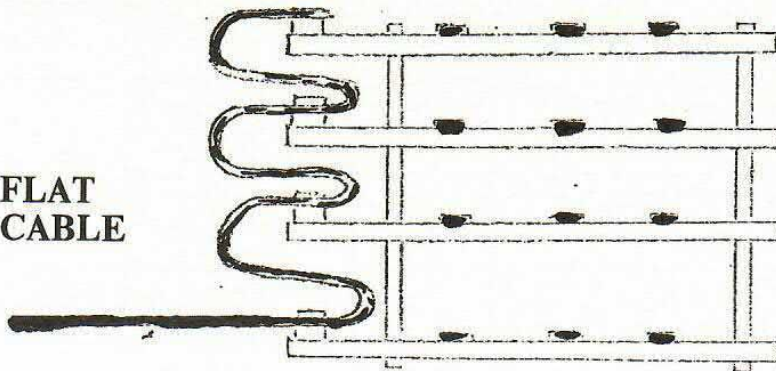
Quattro piastre a sandwich: collegamento con flat cable.
